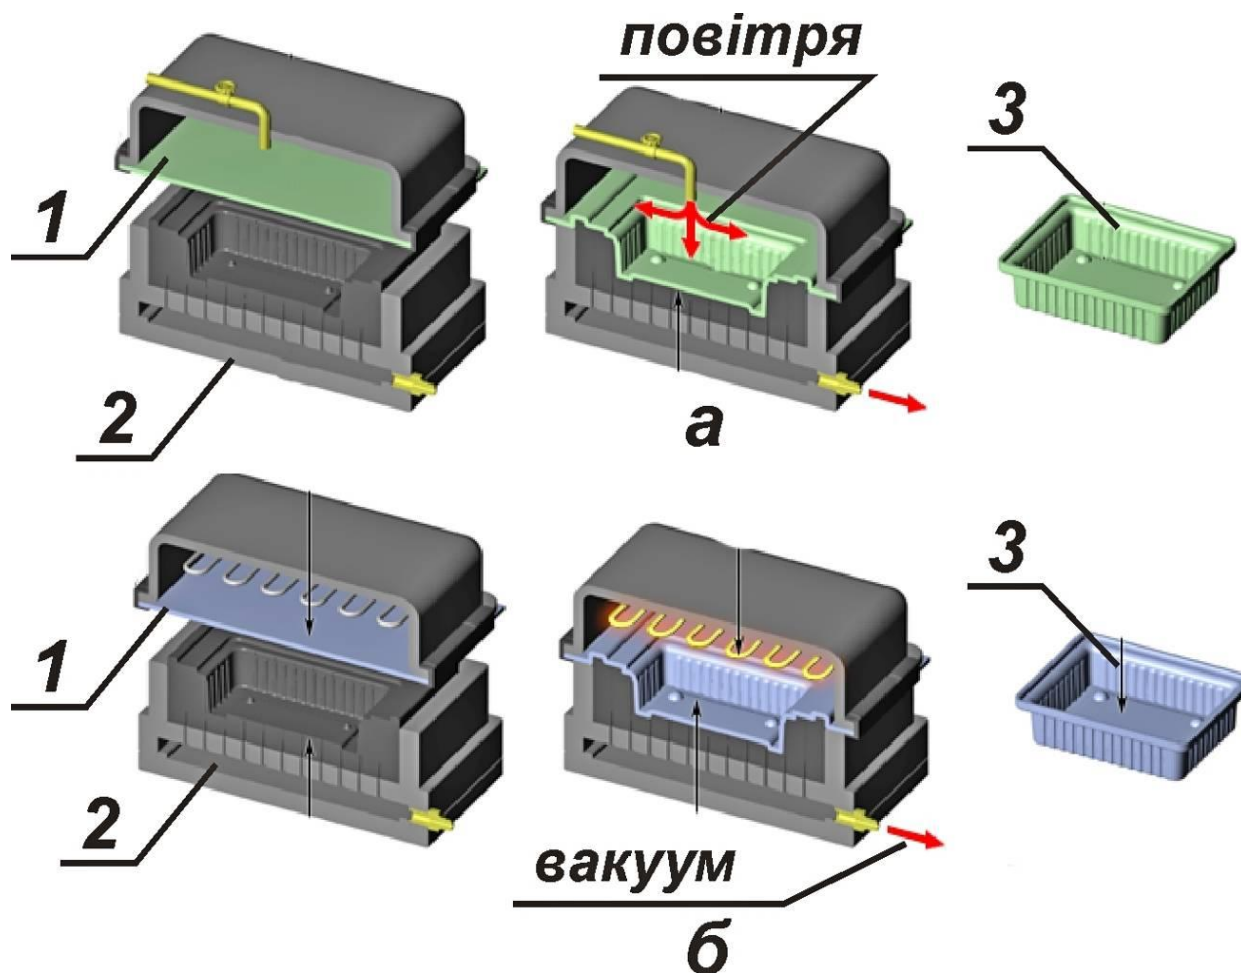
Схема пневматичного (а) та вакуумного (б) формування заготовок з листових пластмас:
